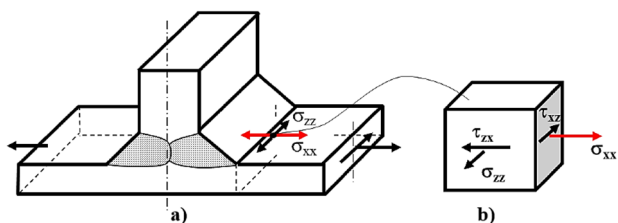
Напряженное состояние в области носка сварного шва а) общая геометрия сварного соединения; б) напряженное состояние в области носка сварного шва
